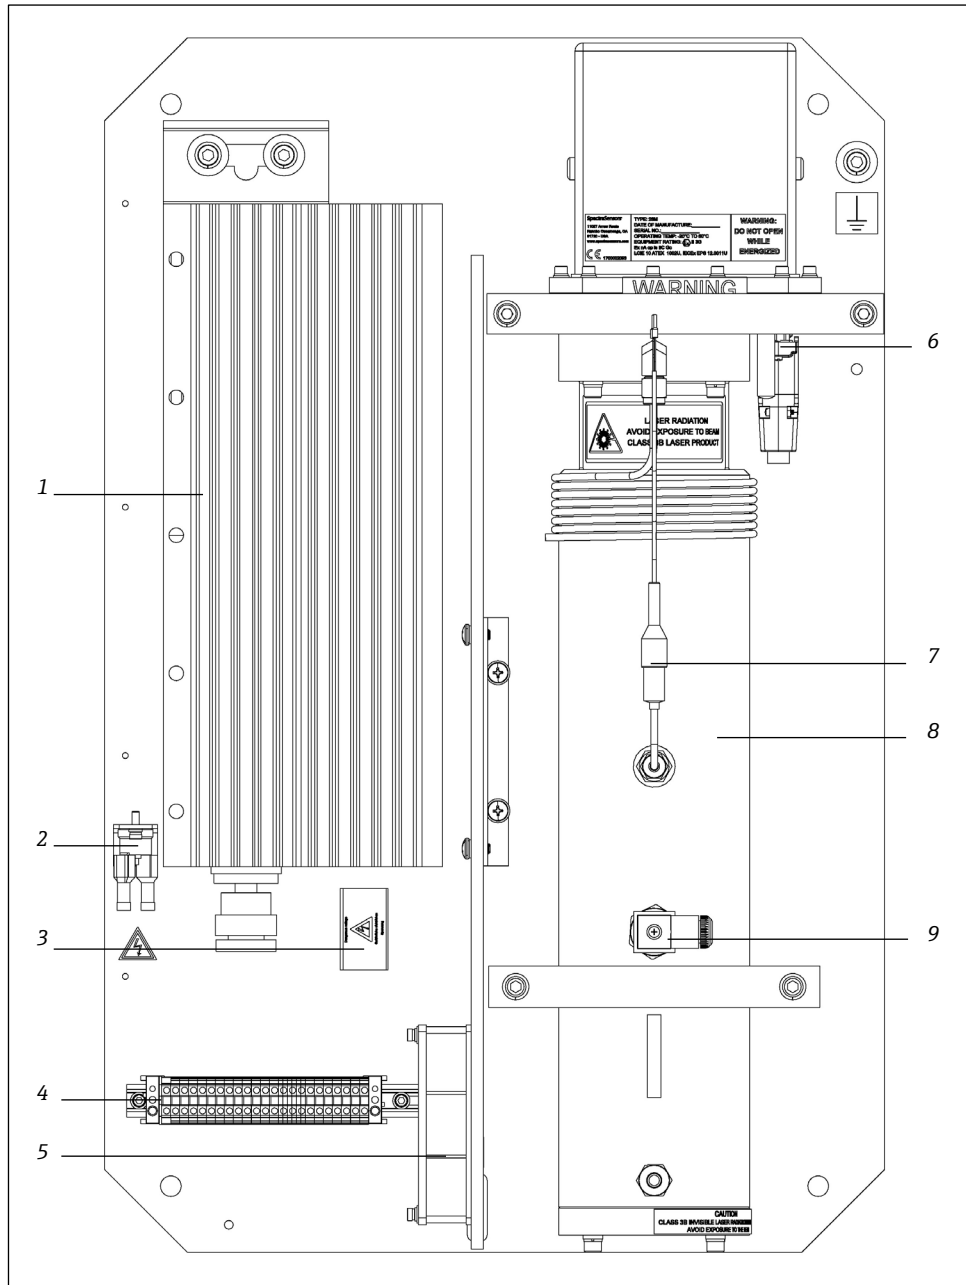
Komponenten in einem 8- oder 28m-Messzellegehäuse
